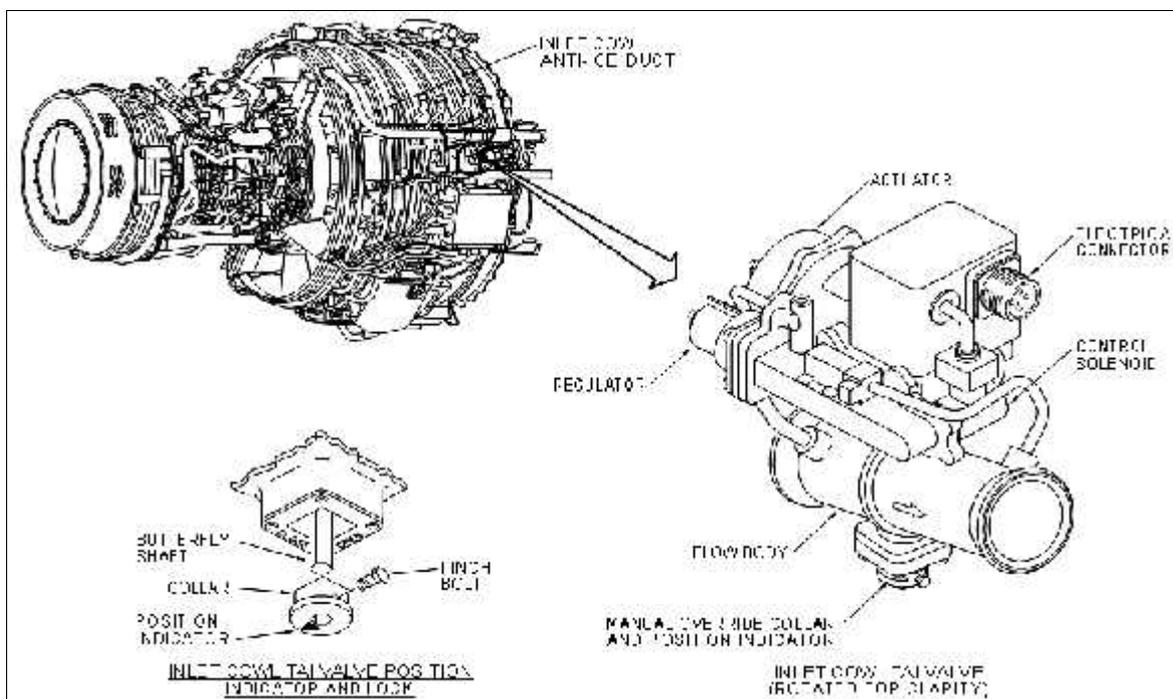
La valve du capot d'entrée d'air moteur
